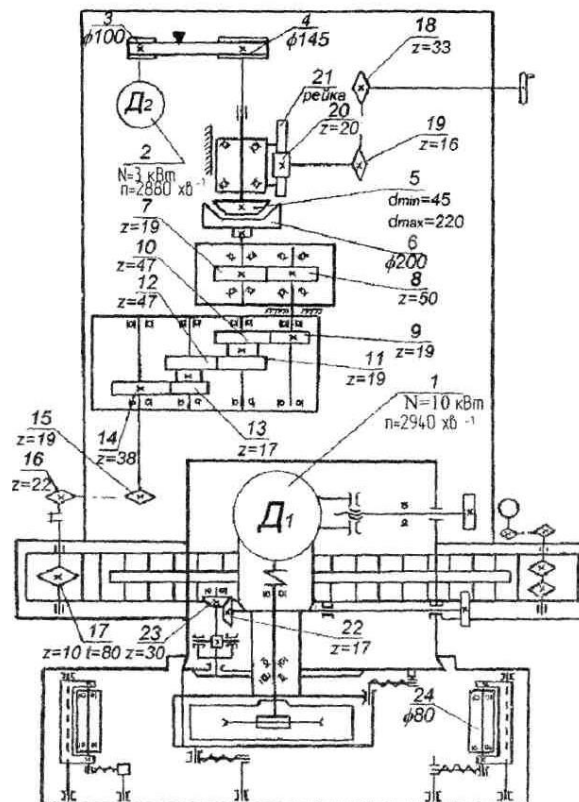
Кінематична схема круглопилкового прирізного верстата моделі ЦДК4-2: 1 - електродвигун механізму різання; 2 - електродвигун механізму подачі; 3, 4 - шківів; 5, 6 - варіатор; 7, 8 - редуктор, що коливається; 9...14 - нерухомий редуктор; 15, 16, 18, 19 - зірочки; 17 - приводний туєр; 20 - шестірня; 21 - зубчаста рейка; 22, 23 - конічна передача; 24 - притискний валець; 25 - лубрекатор
